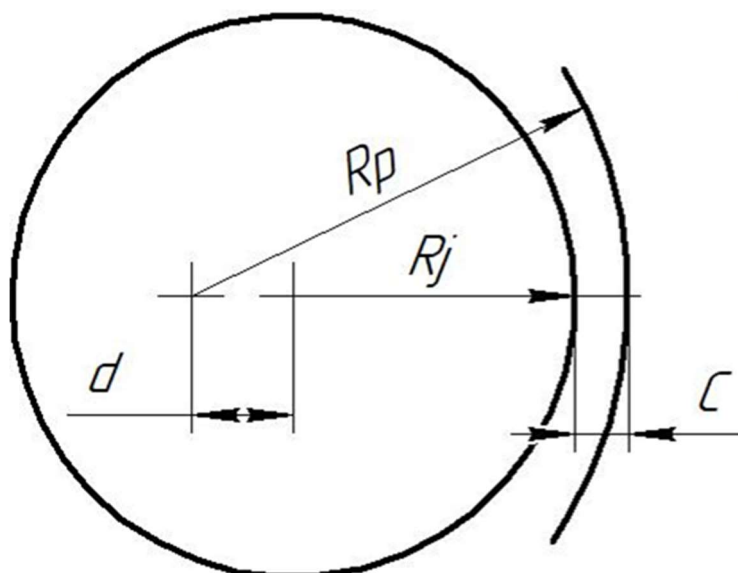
Принципова схема пелюсткового підшипника
